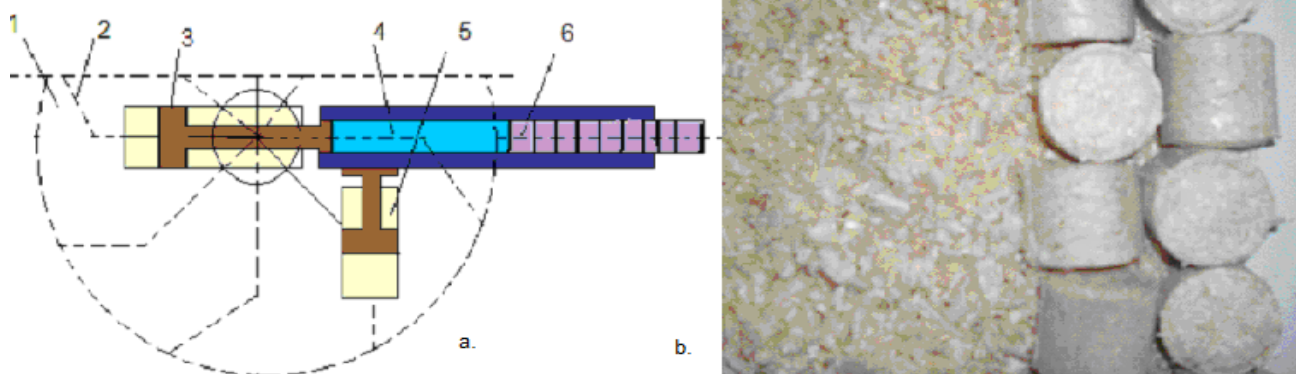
Mașina de brichetat (a) și brichete (b): 1-siloz de stocare; 2-alimentare cu palete; 3- pistonul principal de compresie; 4-canal de extruzie; 5-pistonul secundar de alimentare și compresie; 6-brichete comprimate
